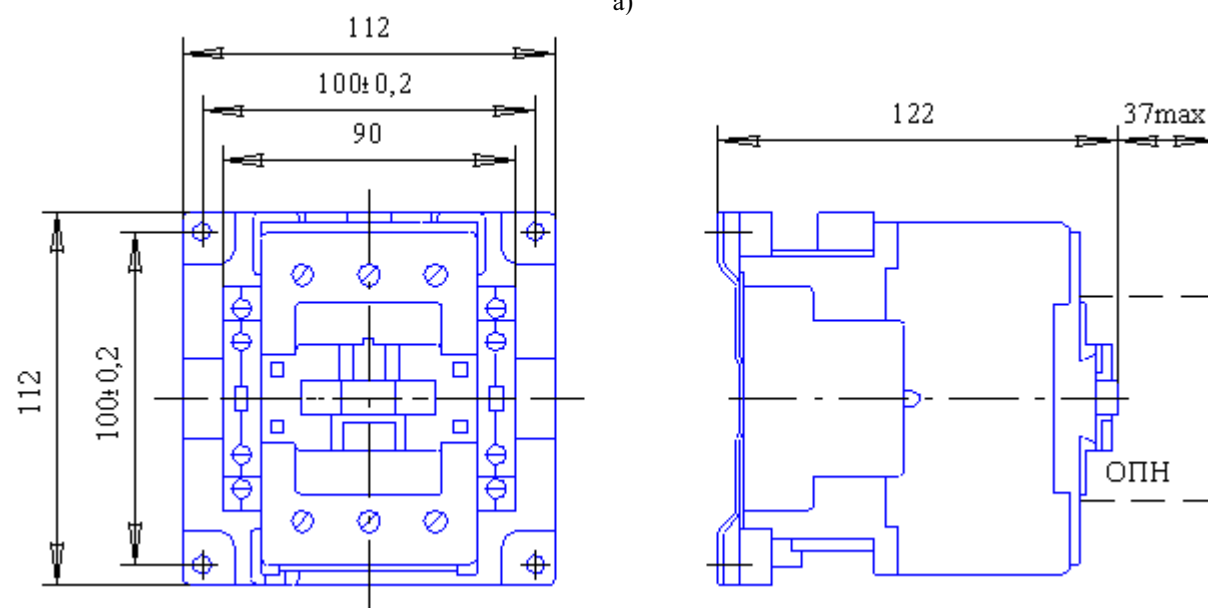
Установочные размеры пускателей типа ПМ12-040:
